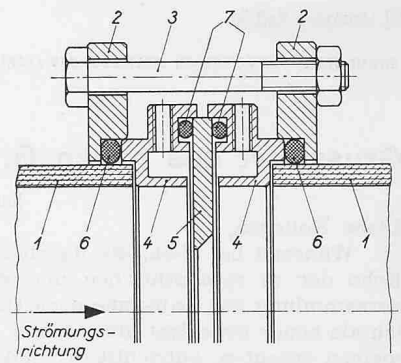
(rechts): Aufbau der Mengenvorrichtung (1 Asbestzementrohre; 2 Flansche; 3 Sechskantschrauben mit Muttern; 4 Ringkammern mit Bohrungen zur Wirkdruckentnahme; 5 Messblende; 6 Dichtungsringe aus Gummi; 7 O-Ringe)
